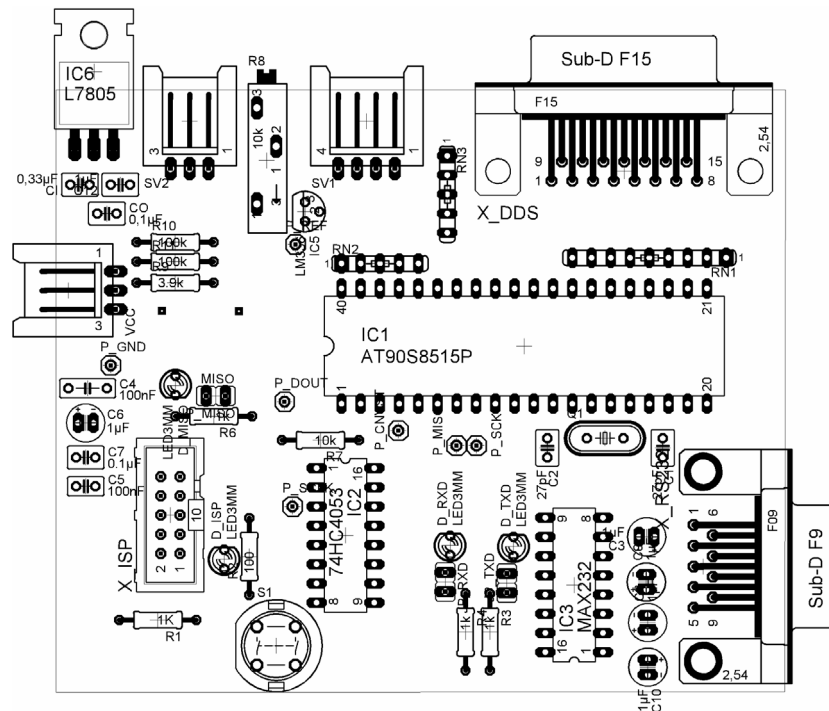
Obere Bestückungsansicht des Platinen-Layouts (Top-Layer)
